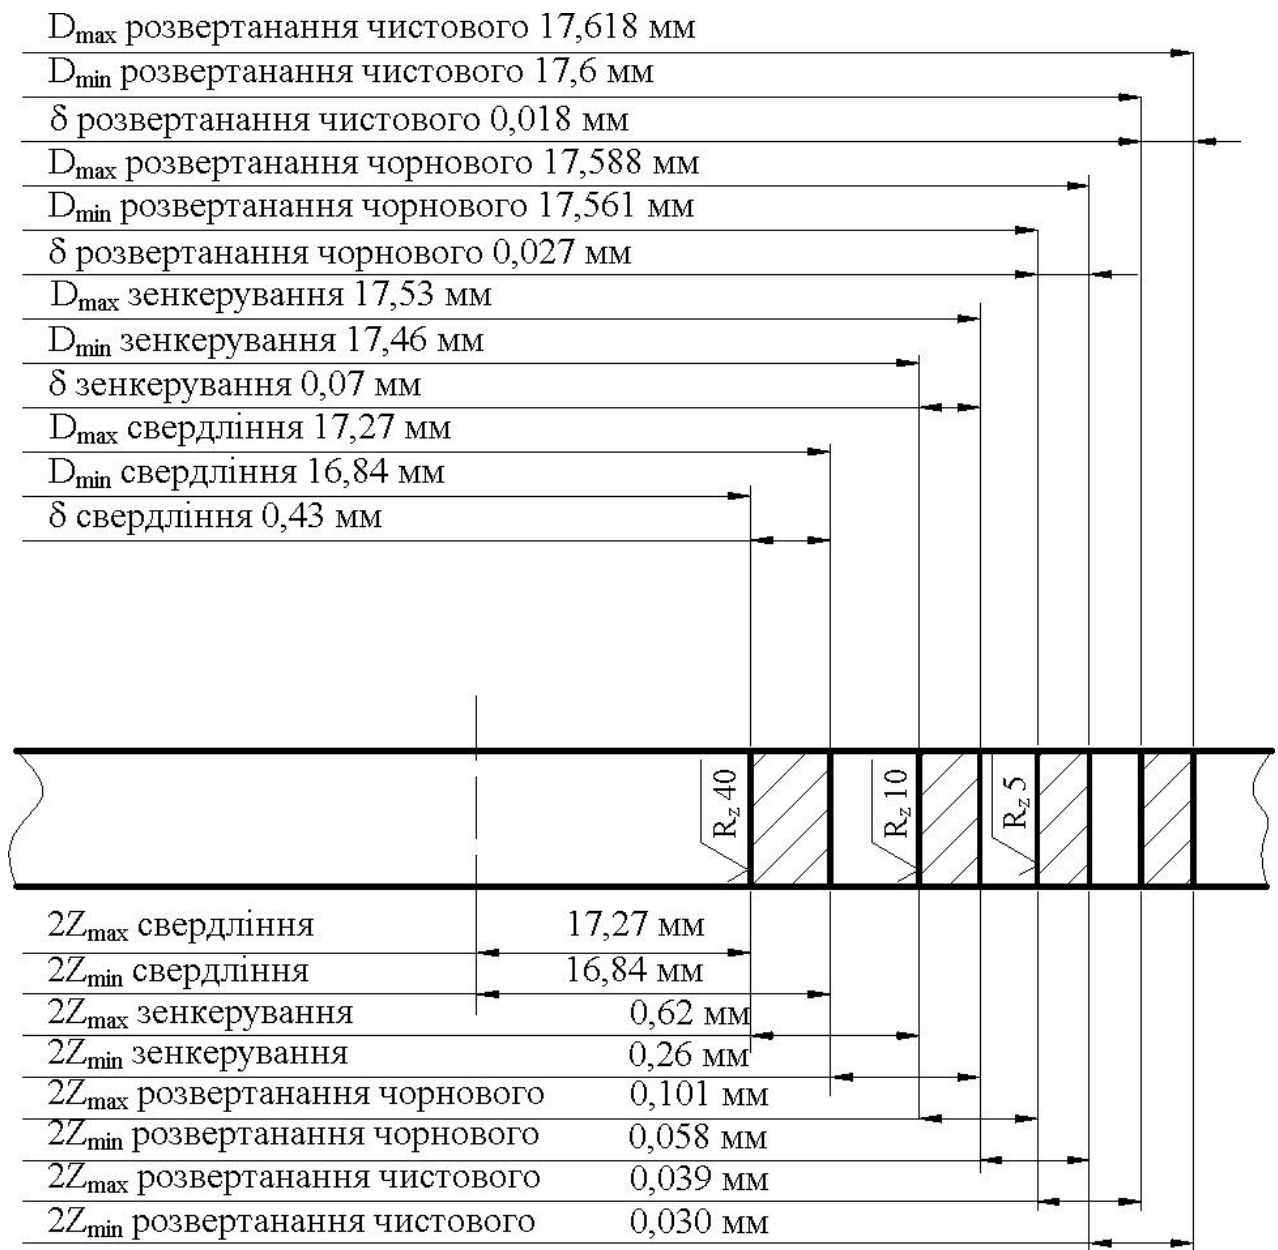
Схема графічного розташування припусків для поверхні  $\varnothing 17,6H7$
